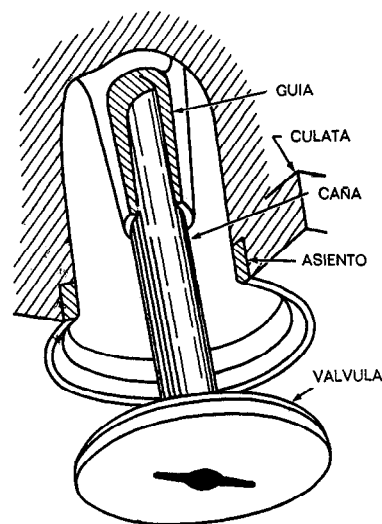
Válvula y asiento de válvula cortado en la culata. La culata, asiento y guía se representan parcialmente cortados para mayor claridad.
